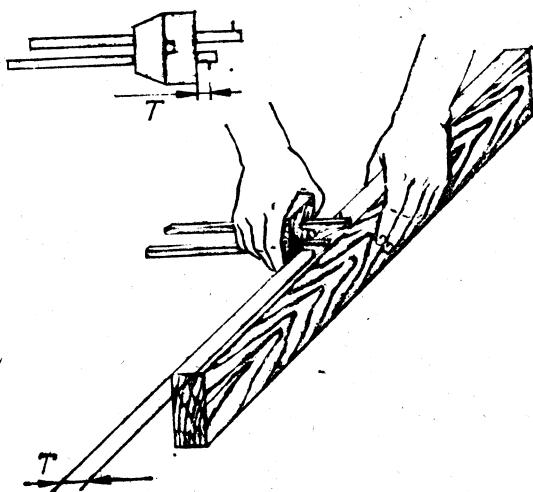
Разметка толщины заготовки с помощью рейсмуса
